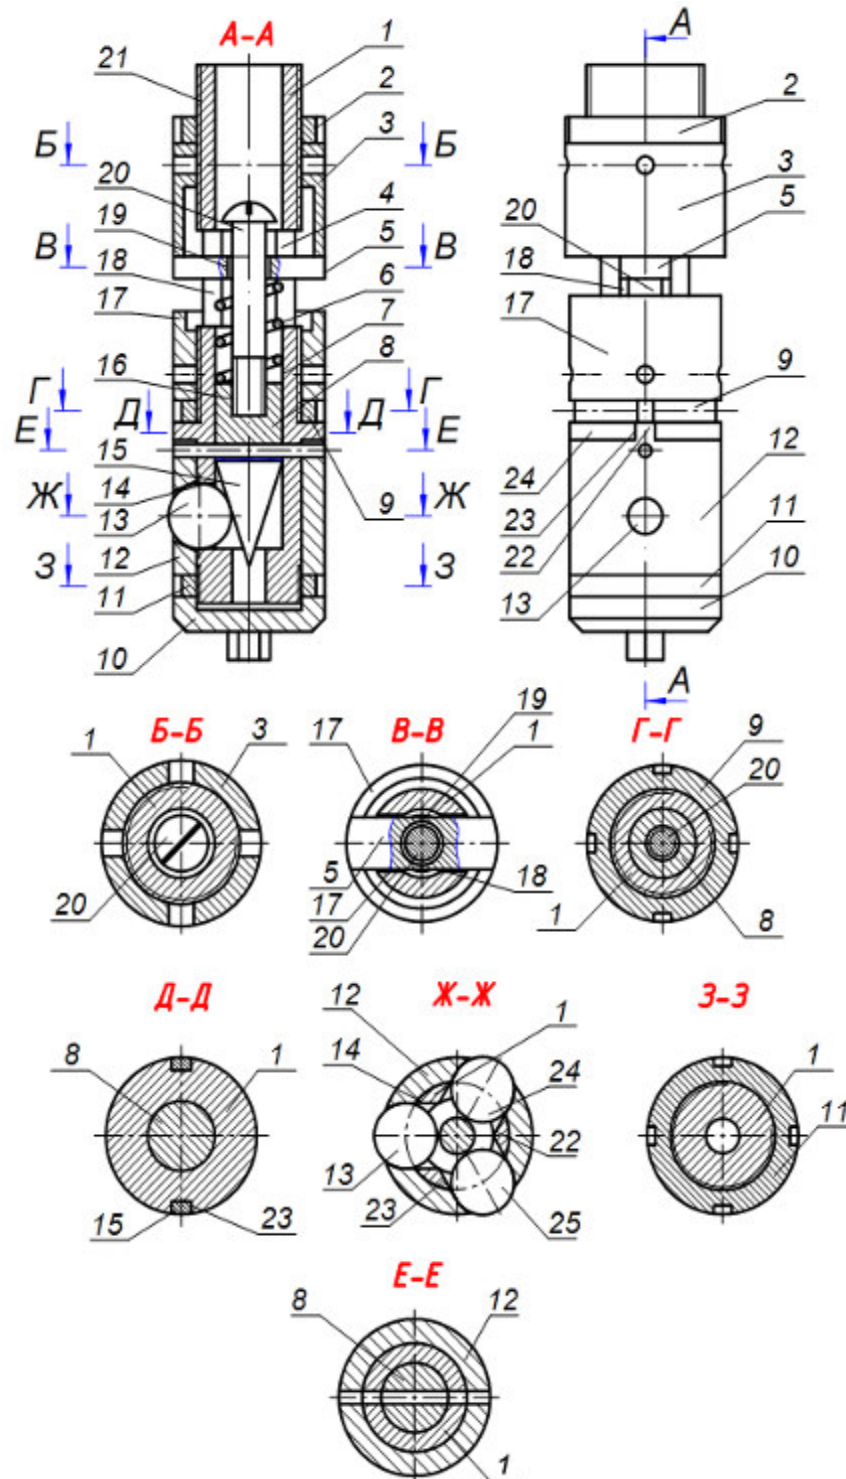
Інструмент для формування регулярного мікрорельєфу віброобробчуванням
